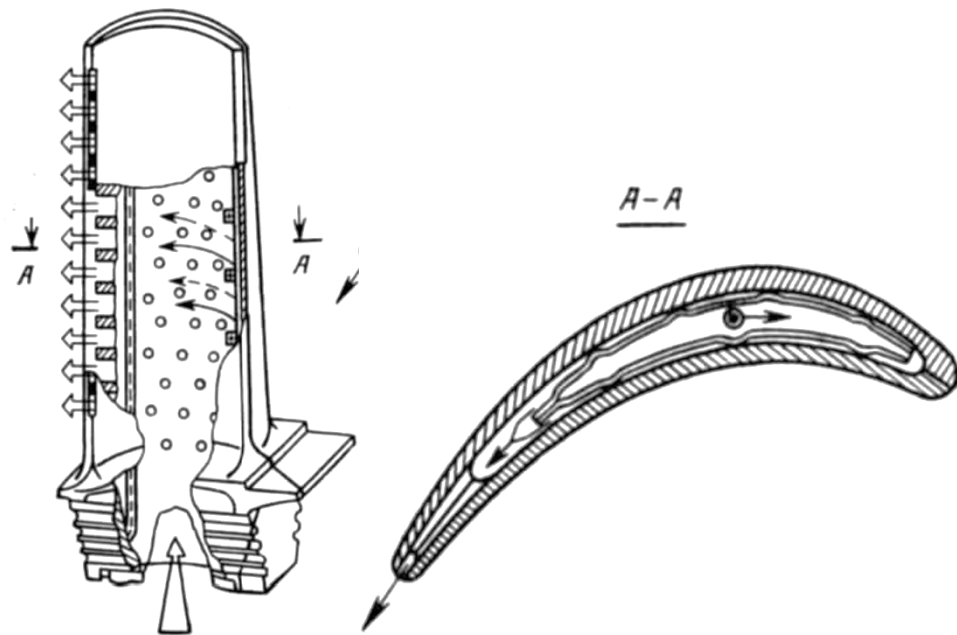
Конструктивна схема звареної з двох частин лопатки з дефлектором.
